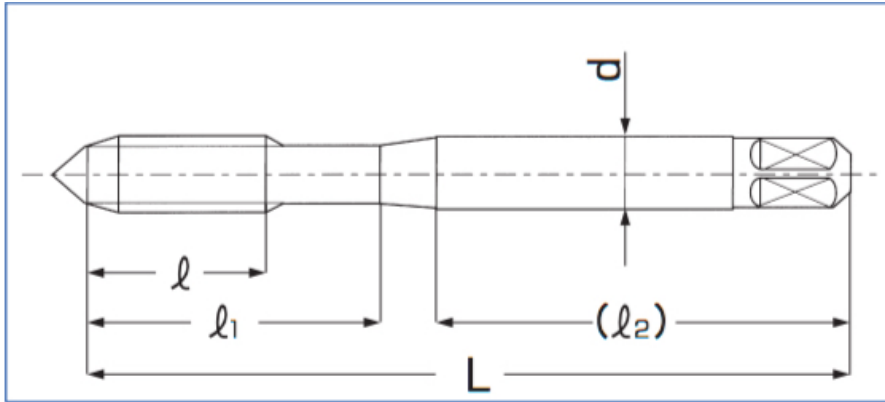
Bildmaterial von Gewindebohrer, Quelle: Internet
